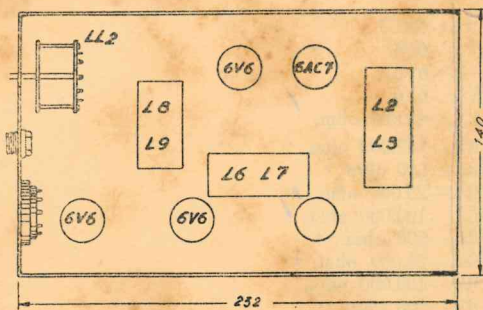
Distribución de piezas y dimensiones del chasis del O. F. V.
